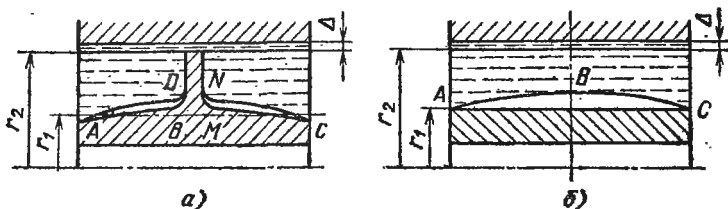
Поперечное сечение рабочей ячейки в области минимального зазора между колесом и корпусом:
